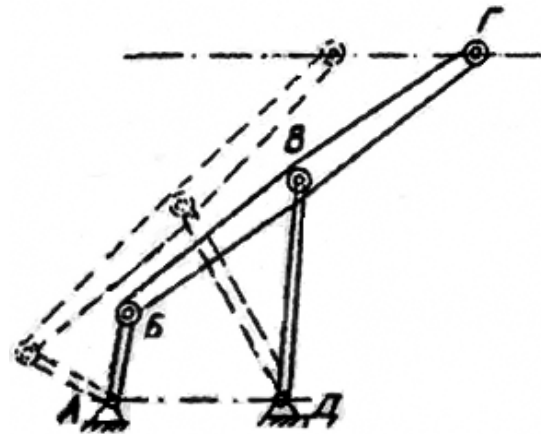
Кинематическая схема четырехзвенного направляющего механизма
